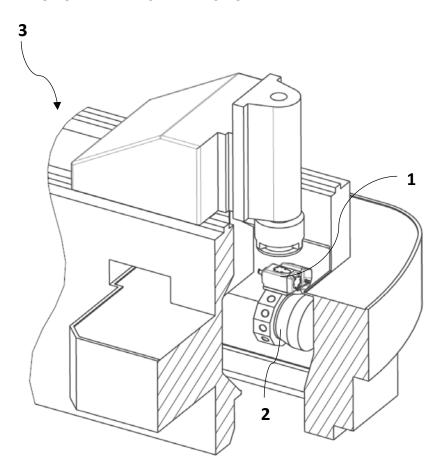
Drehmaschine mit ausgerüsteten Werkzeugsystem
